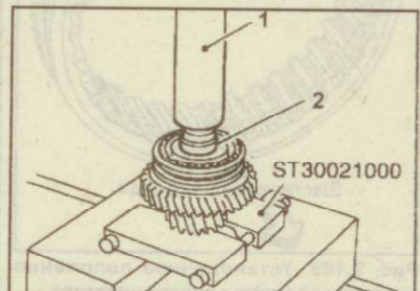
Использование оправки (1) для установки втулки шестерни 2-й передачи (2)
